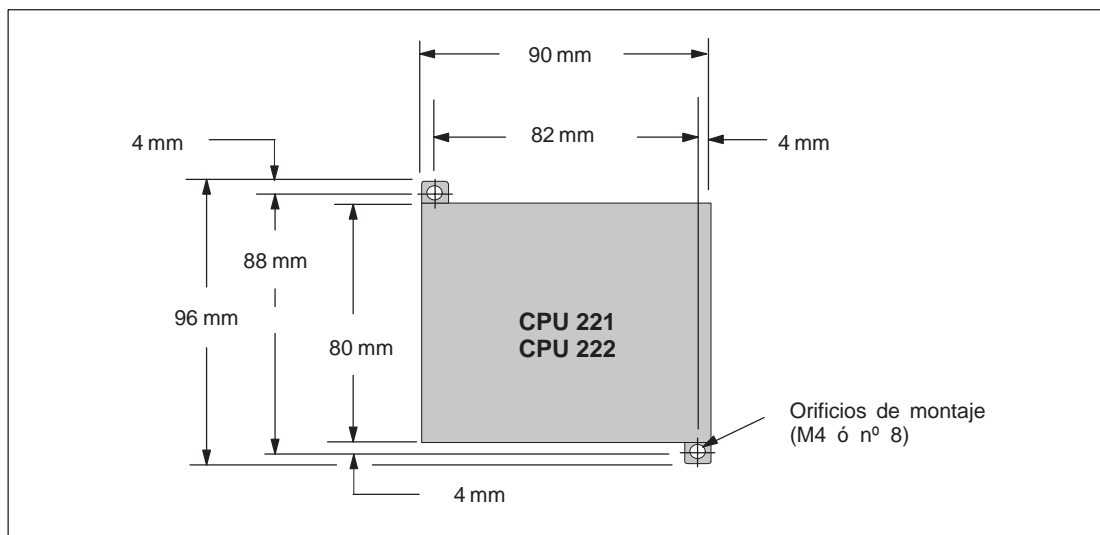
Dimensiones de montaje para una CPU 221 y una CPU 222
